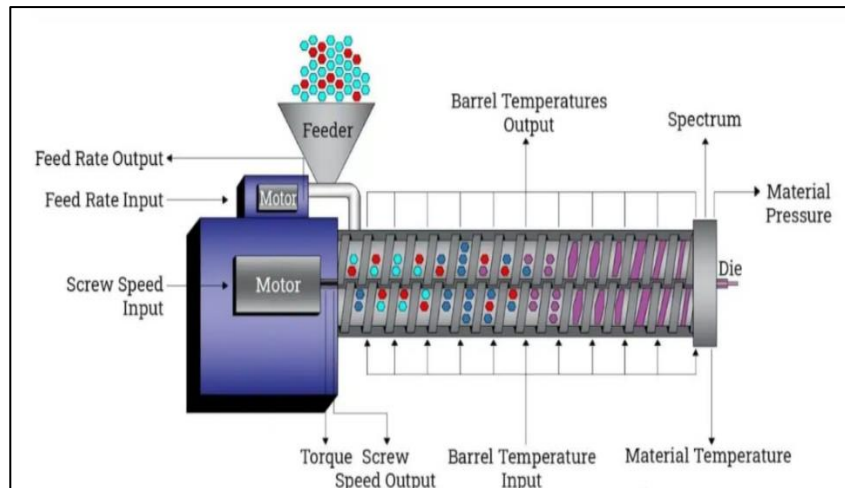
Extruder μονού κοχλία [Πηγή : (<https://www.useon.com/machine/single-screw-extruder/>, n.d.)]
